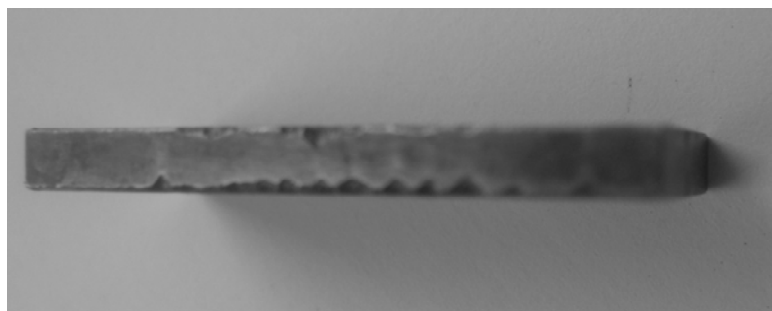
Характер разрушения рабочей поверхности ножа-прототипа для рубки фибры на станке G8010
